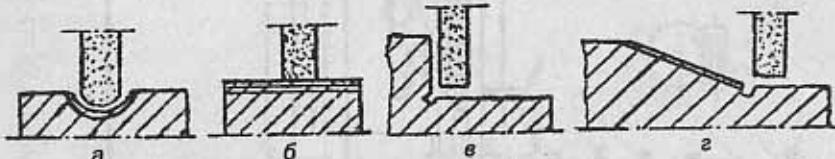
Схемы обработки на круглошлифовальном станке с ЧПУ
